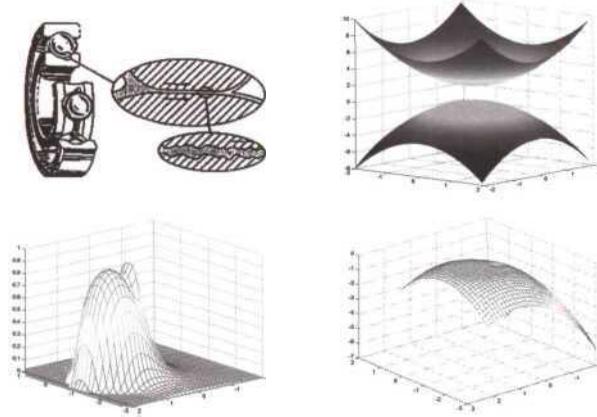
CONTACTO LUBRICADO AISLADO DE UN ELEMENTO DE MÁQUINA
